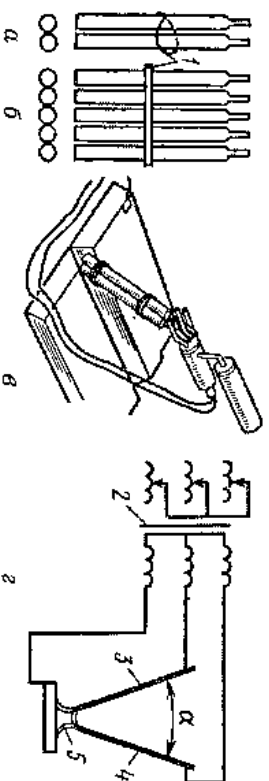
Схема сдвоенного электрода (а), гребёнки (б) и сварки трехфазным током (а, б): 1 — свазка электродов, 2 — трехфазный трансформатор, 3, 4 — электроды, 5 — дуга
